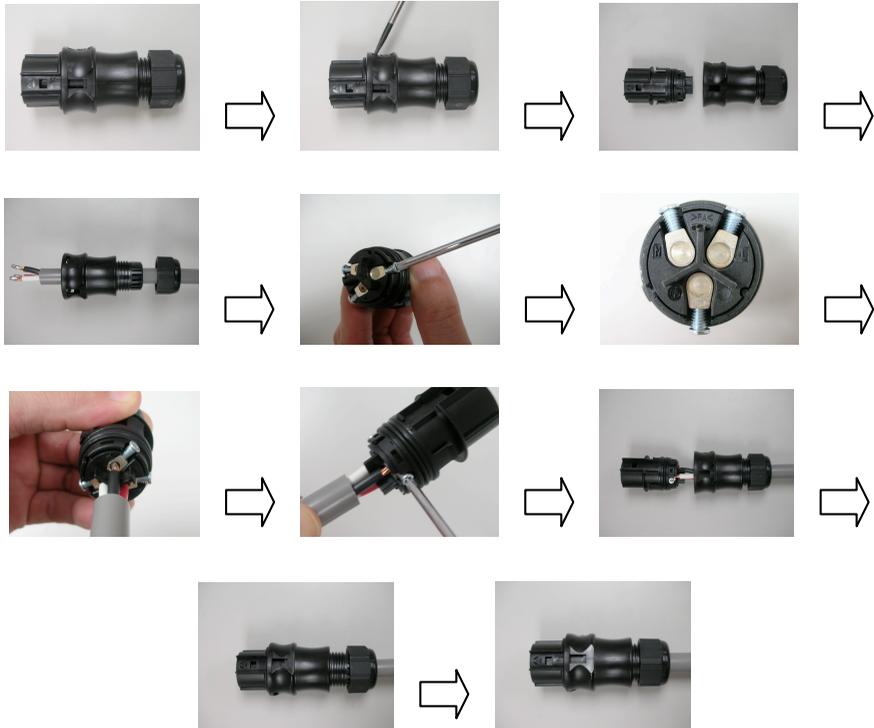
Ensamblaje del cable y del conector CA
